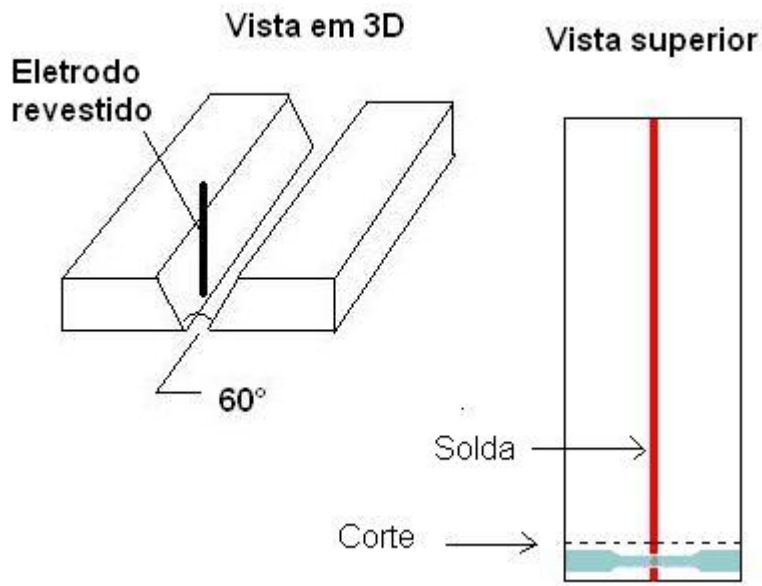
Procedimento de soldagem e confecção dos corpos de prova.
